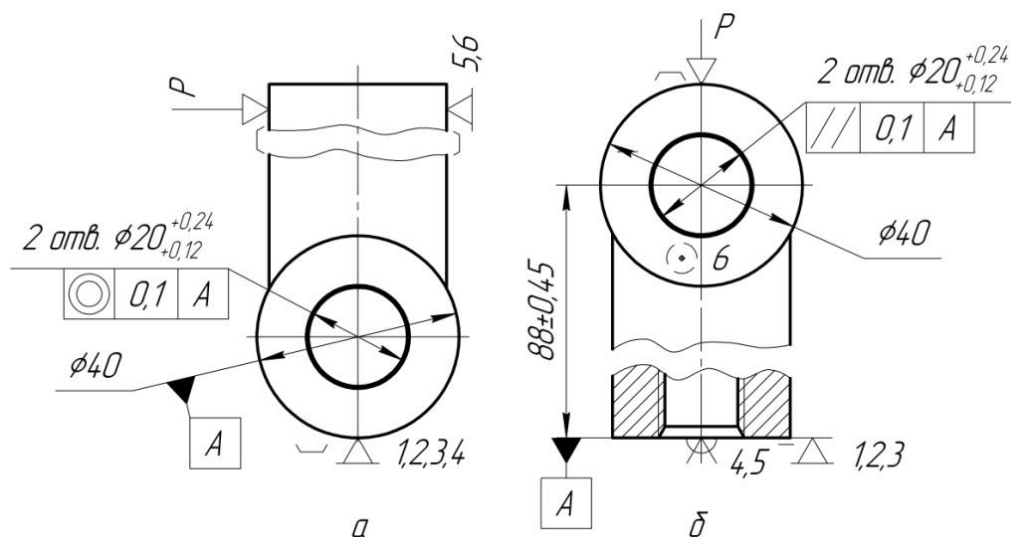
Схеми базування заготовки на другому верстаті:
